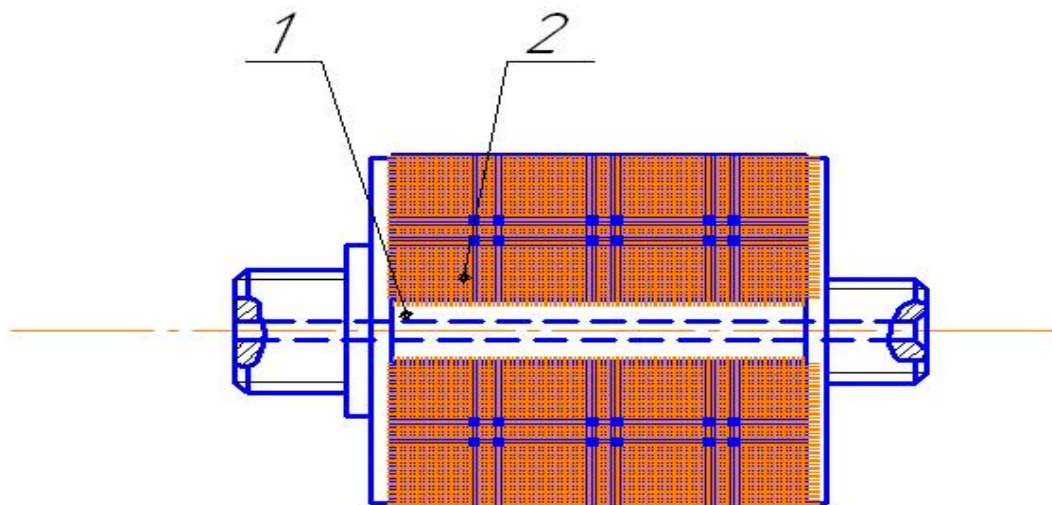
Схема пристрою для обробки палива перед згорянням.
